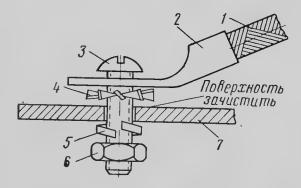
Типовое крепление перемычки металлизации с помощью болта и гайки:
